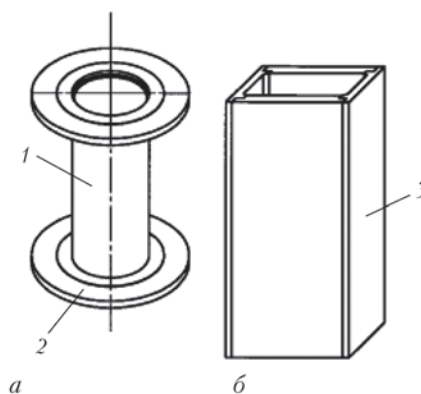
Конструкции кристаллизаторов, изготовленных ковкой из слитков: а — кованый бесшовный (1) с приваренным фланцем (2); б — состоящий из четырех отдельных листов (3)
